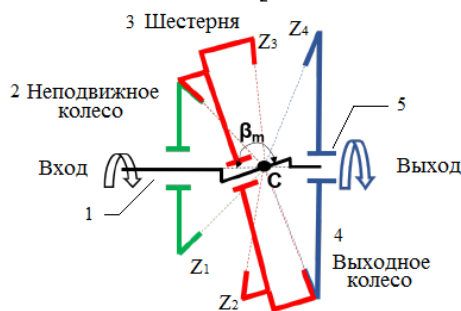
Принципиальная схема волнового торцевого кинематического редуктора
